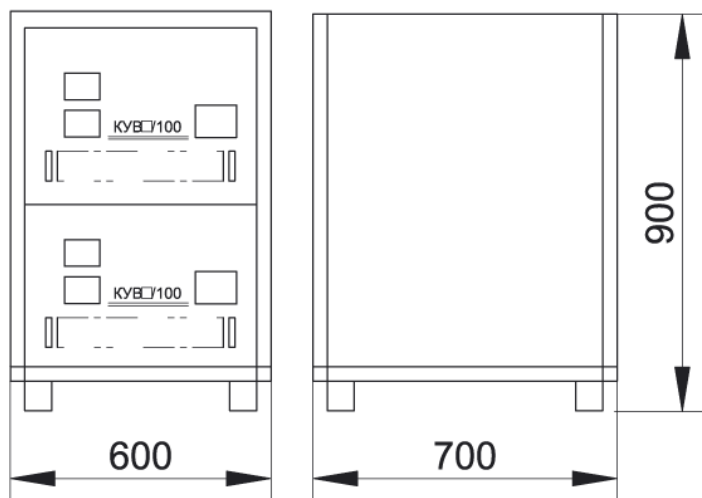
(б). Габаритный чертеж конвертора КУВ-2 (пятыместный каркас)
